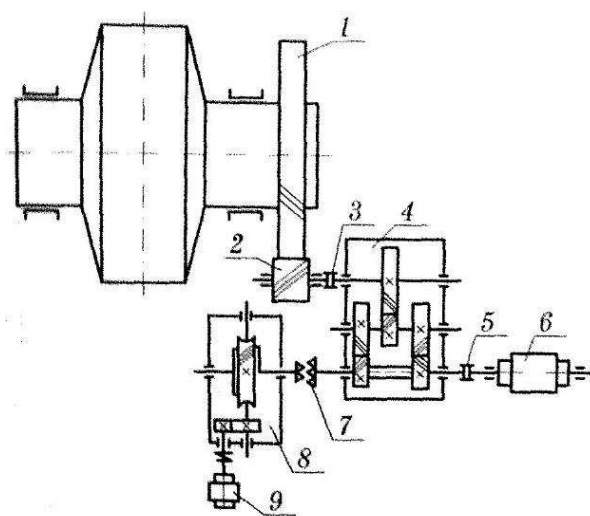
Кинематическая схема привода мельницы ММС
